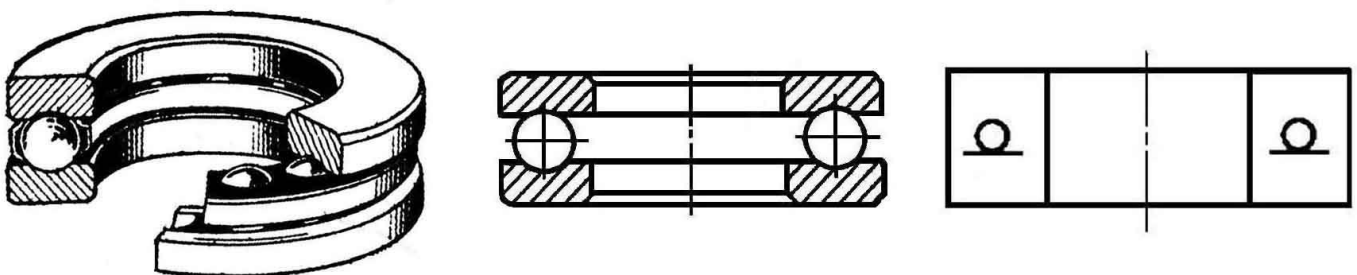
Підшипники кулькові упорні типу 8000
